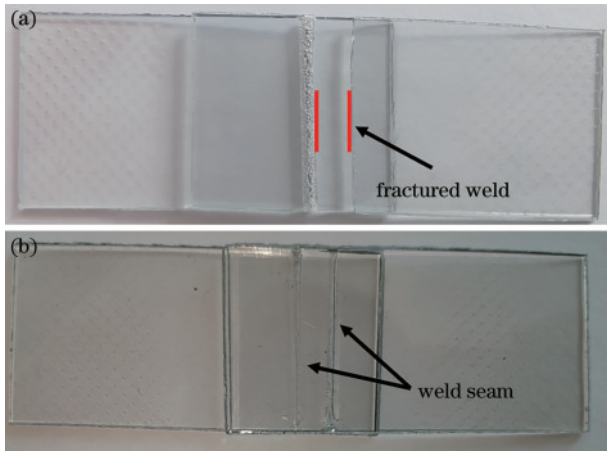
拉力测试后的焊接试样。(a)焊缝断裂;(b)焊缝分离
